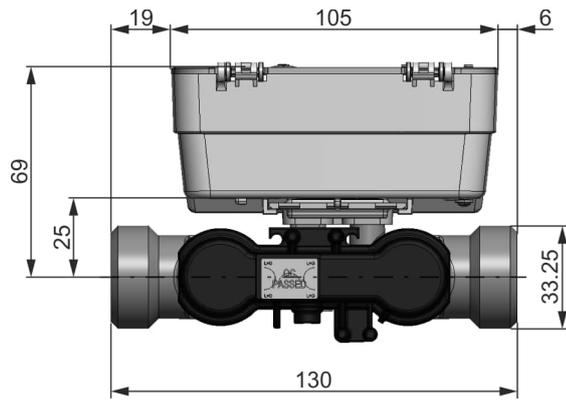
Abb. 4: Übersicht Masse Baulänge 130 mm (Gewinde)
